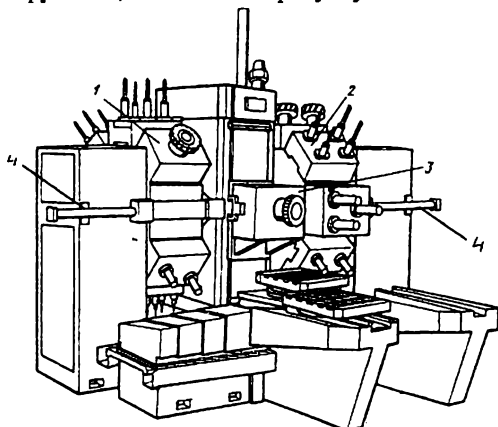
Компонівка багатошпindelного верстата з двома магазинами барабанного типу:
